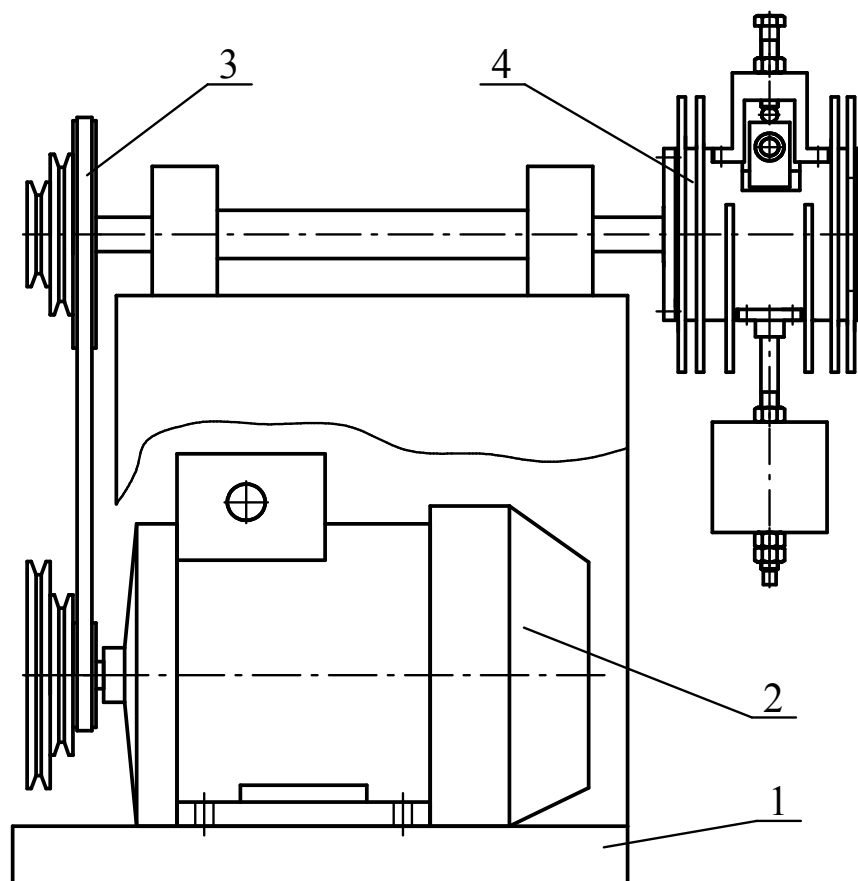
Общий вид установки для проведения ресурсных испытаний: 1 – корпус установки, 2 – электродвигатель, 3 – ременная передача, 4 – подшипниковый узел в сборе
